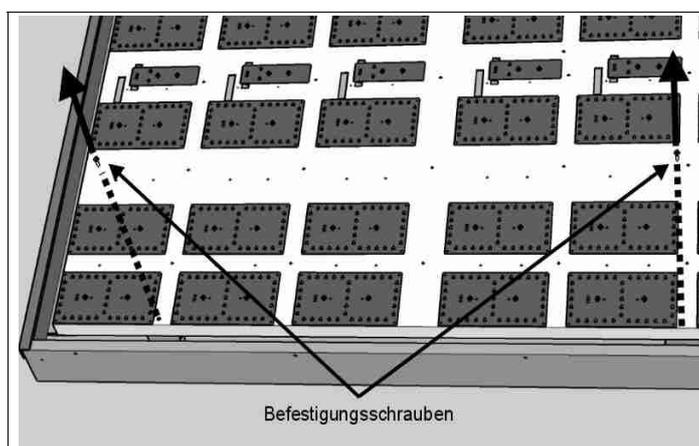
Befestigungsschrauben der LED-Platinen Halterung
